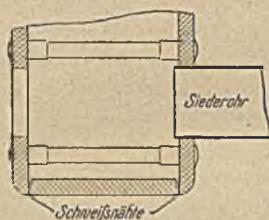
Unvollkommene Schweißung des Umlaufbleches.
